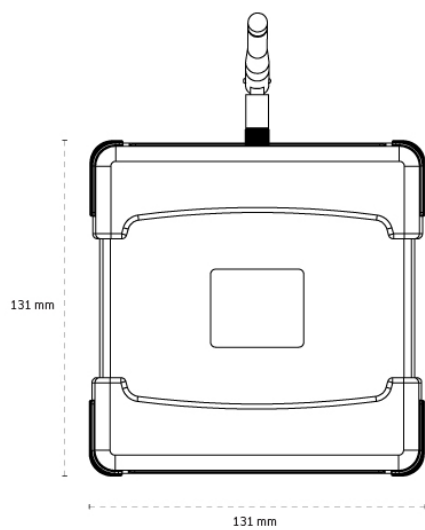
Dimensões do Universal IoT Gateway com caixa de ABS
